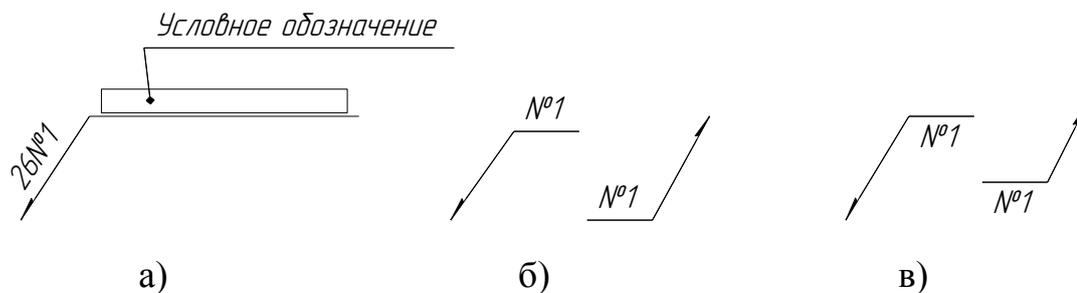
Обозначение одинаковых сварных швов на чертеже [24]
